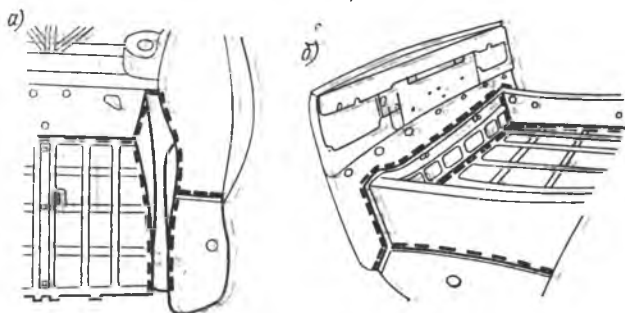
Сварка деталей задка кузова (штриховыми линиями указаны места сварки сопрягаемых деталей): а — задних лонжеронов, пола багажника, пола для топливного бака; б — усилителя задней панели, пола для запасного колеса, пола багажника, задней панели
